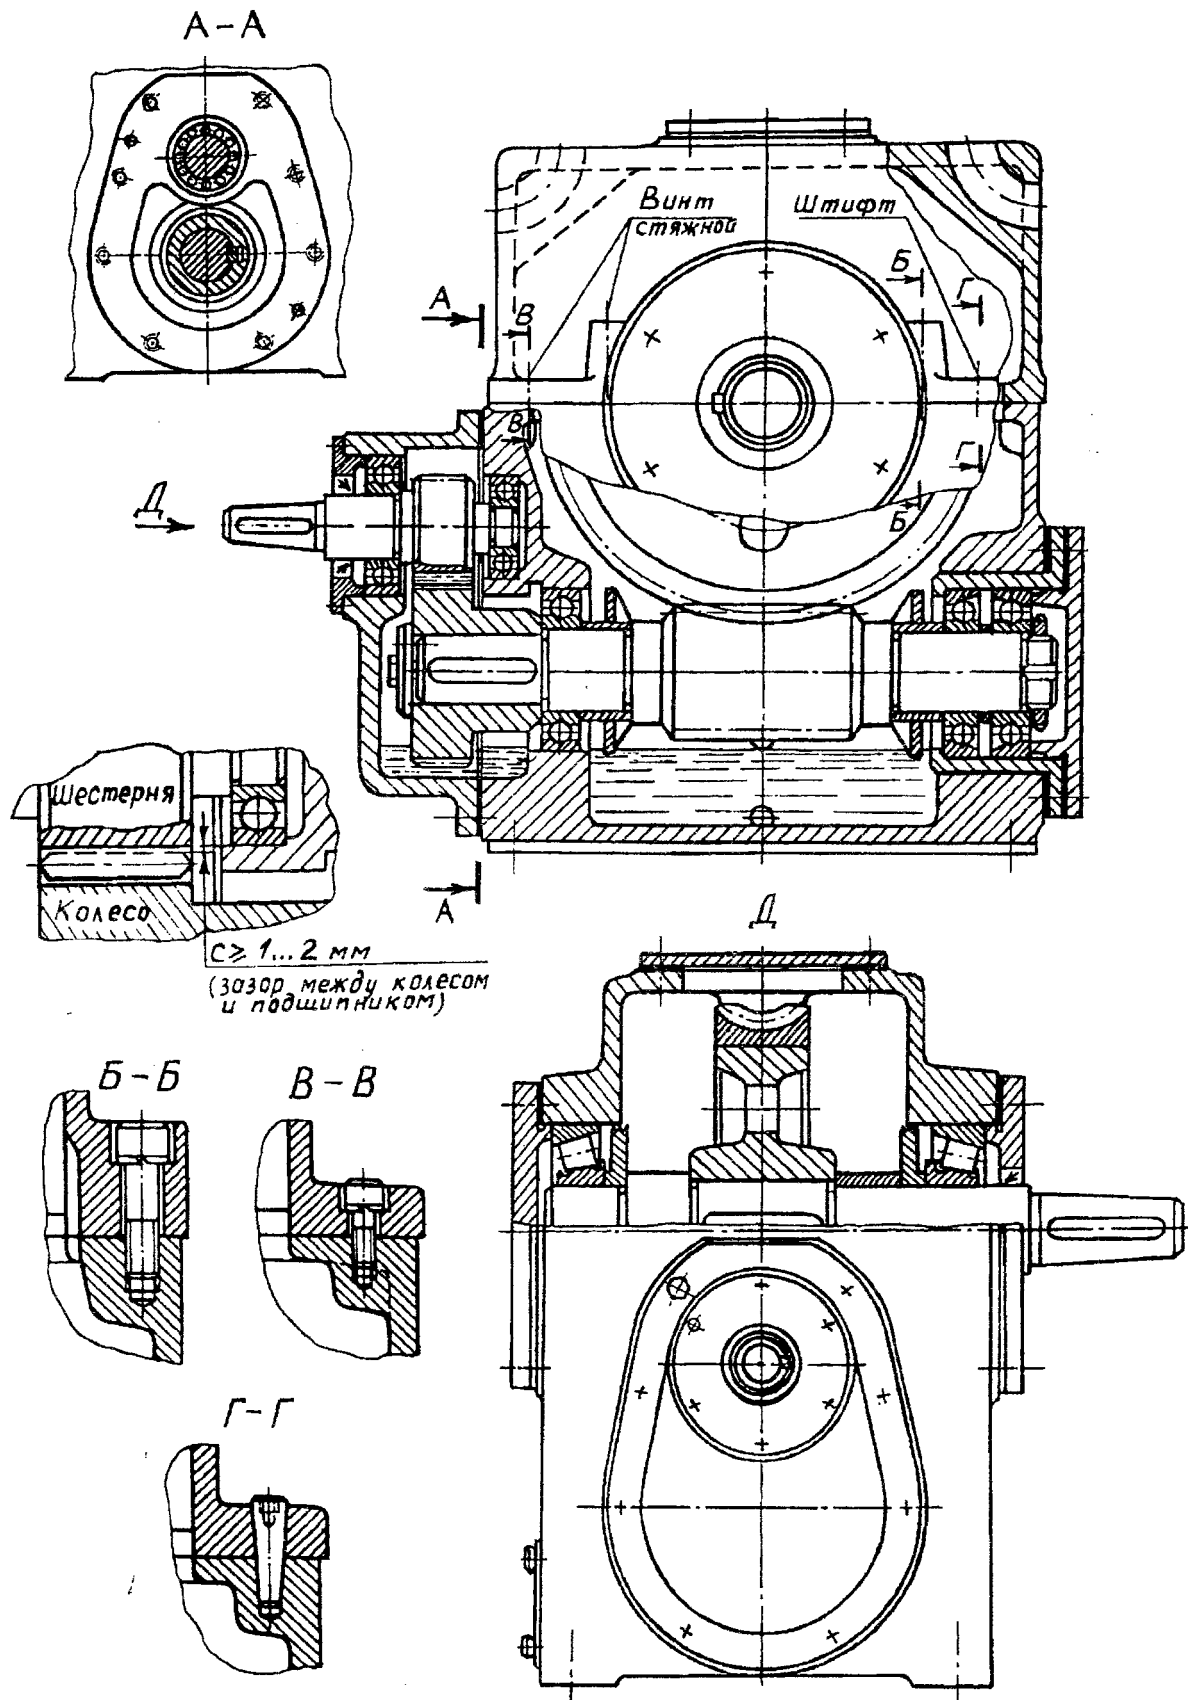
Цилиндрическо-червячный двухступенчатый редуктор
